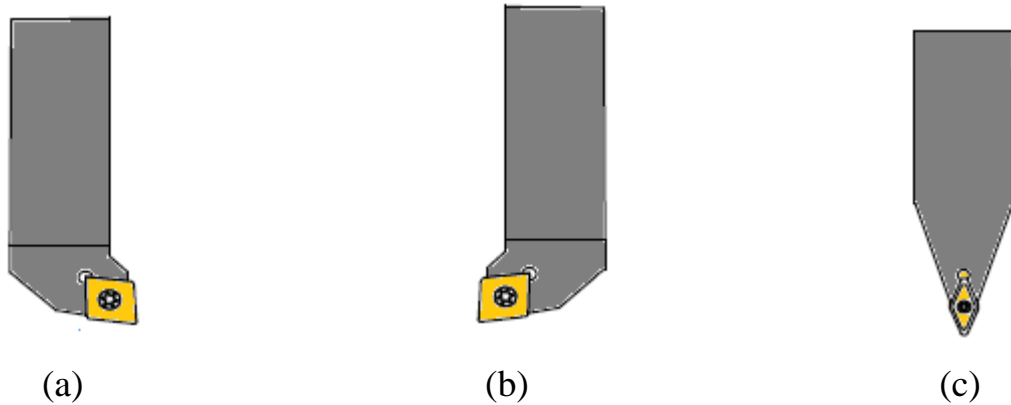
(a) Outil à plaquette en carbure droit R ; (b) Outil à plaquette en carbure gauche L ; (c) Outil à plaquette en carbure neutre.
